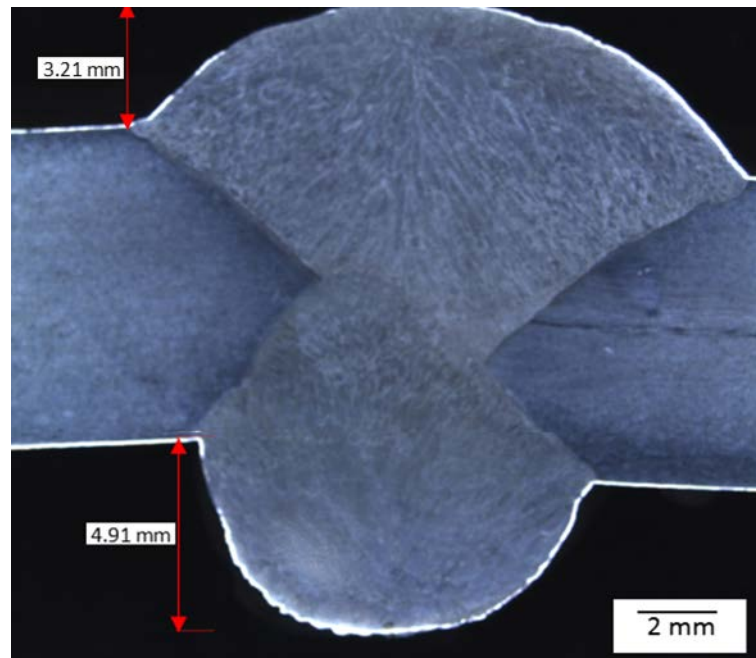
Imagen por macrografía óptica de la soldadura con las dimensiones de las propiedades de la soldadura.
